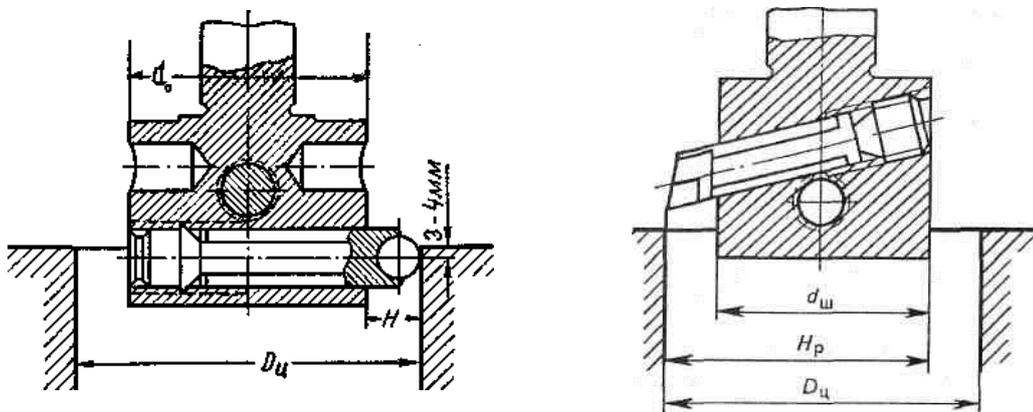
Установка для расточки с использованием оправки с шариком (а) и установка резца (б)
